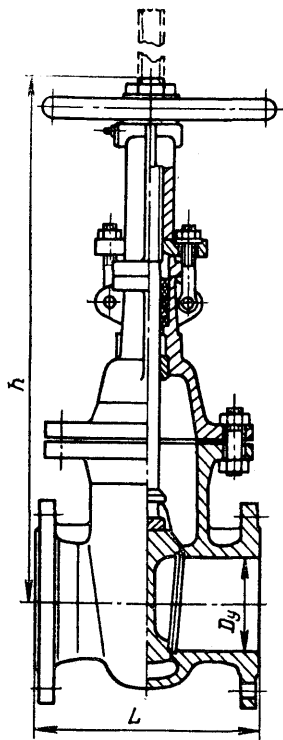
Задвижка стальная клиновная с выдвижным шпинделем ЗКЛ2-16.
